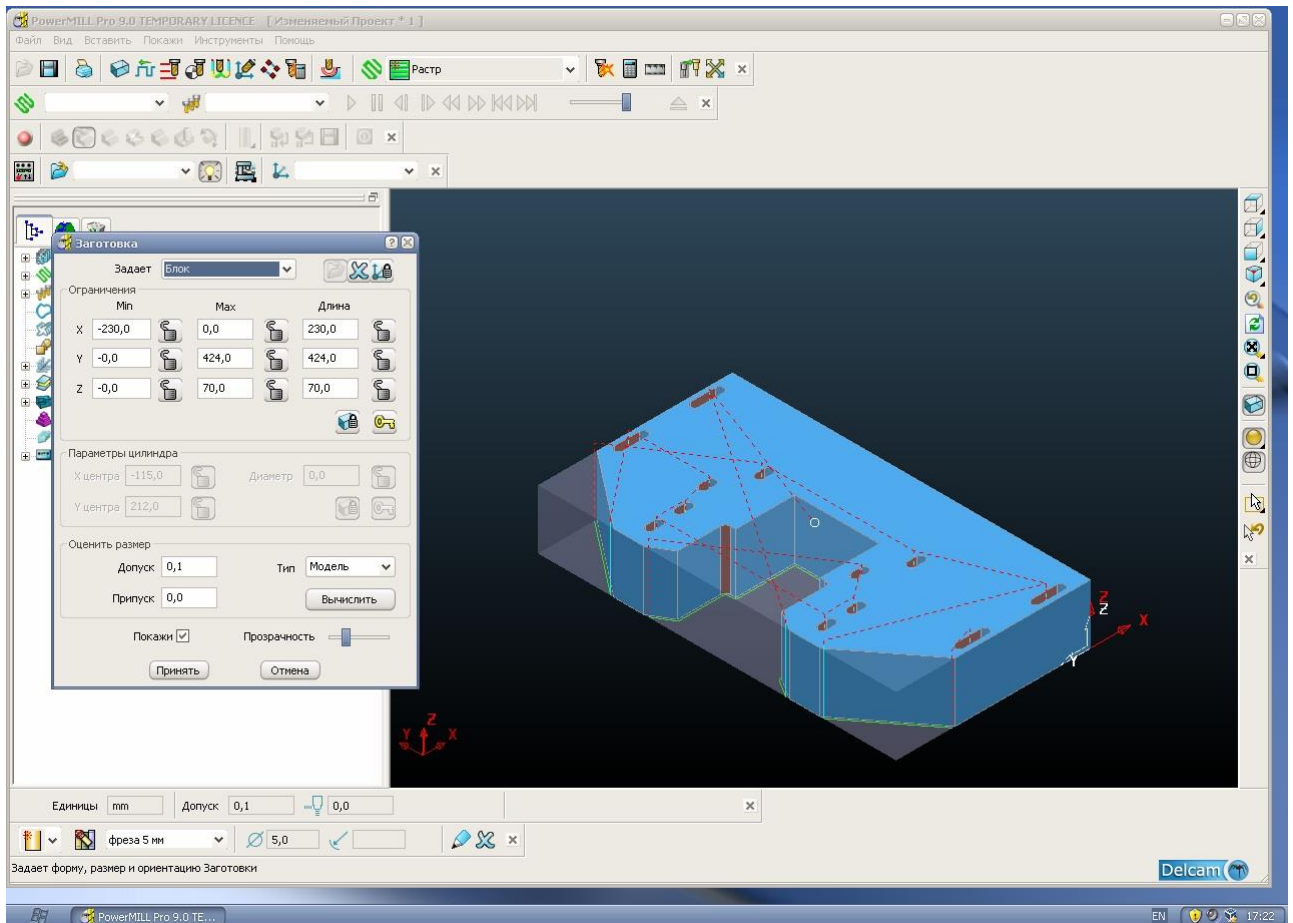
Тривимірна модель заготовки в PowerMill
